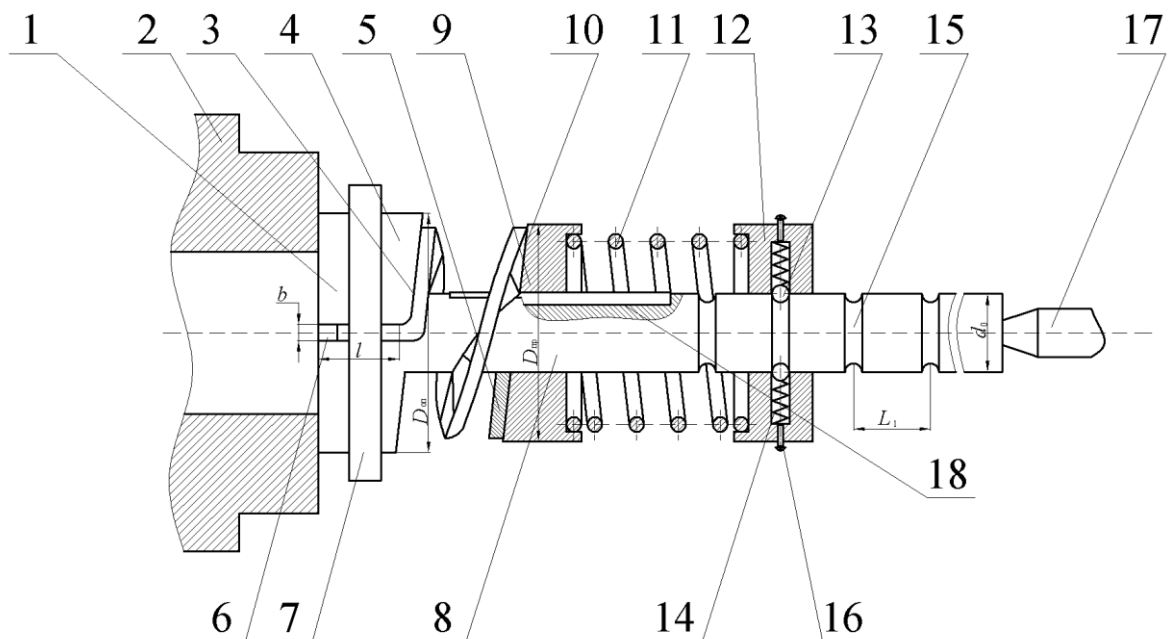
Пристрій для навивання ГГЗ з довільним профілем гофр
